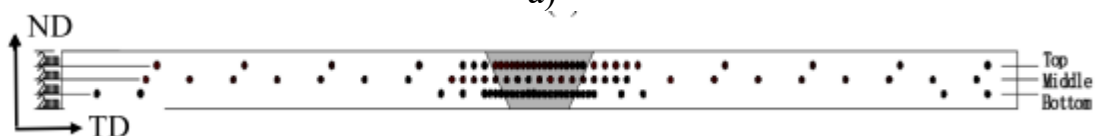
Зразок різнорідного зварного з'єднання ЗТП [21].
